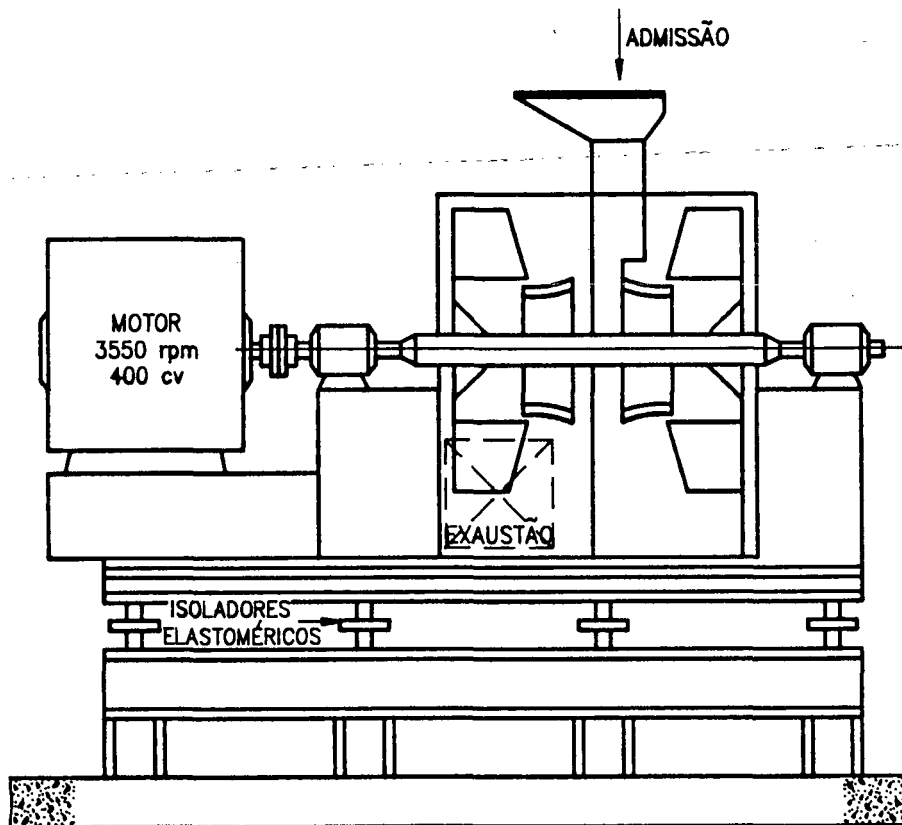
Esquema do conjunto motor/exaustor.
